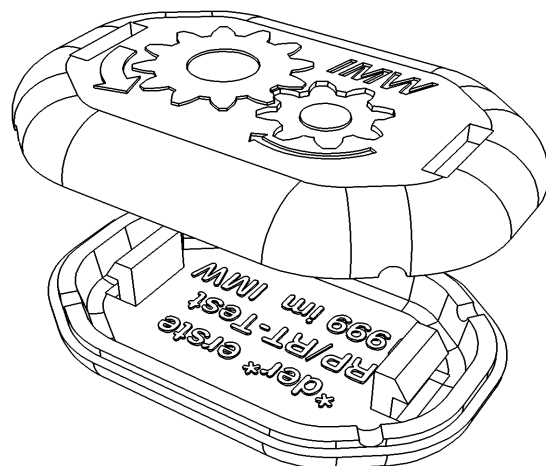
Schlüsselanhänger in Explosionsdarstellung
